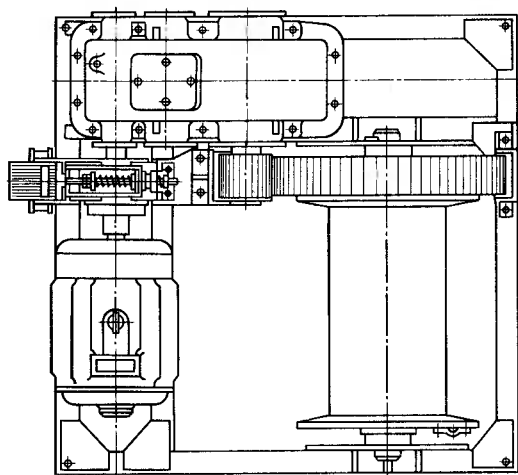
Механизм подъема с открытой зубчатой передачей
